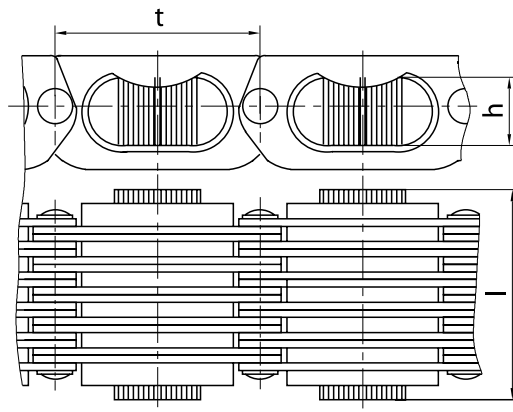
Общий вид цепи для вариаторов типа ВЦ
